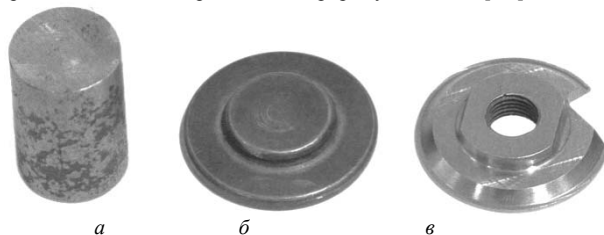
Дисковые резцы из стали Р6М5–МП, полученные в условиях сверхпластического деформирования: *а* – исходная заготовка; *б* – заготовка после СПД; *в* – резец
